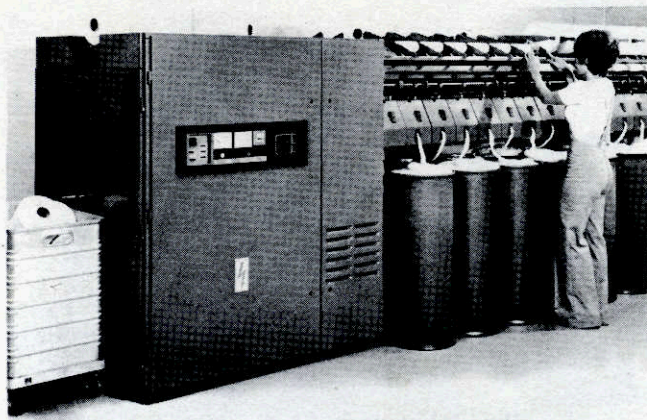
Rotorspinner KU 11 der Firma Schubert & Salzer AG
